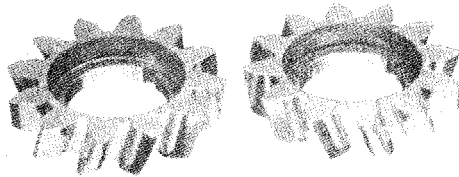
Fresado de engranes (Illinois Tool Works, Chicago, Ill.)
